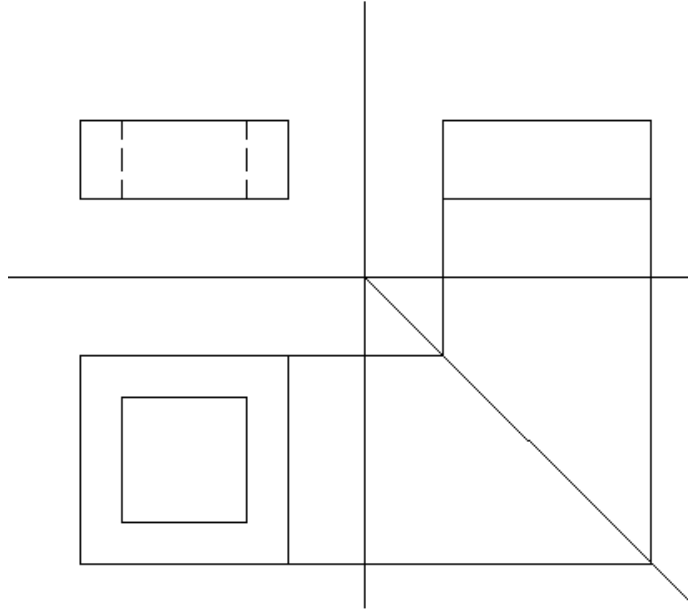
Temel boyutların yatay düzleme taşınması
